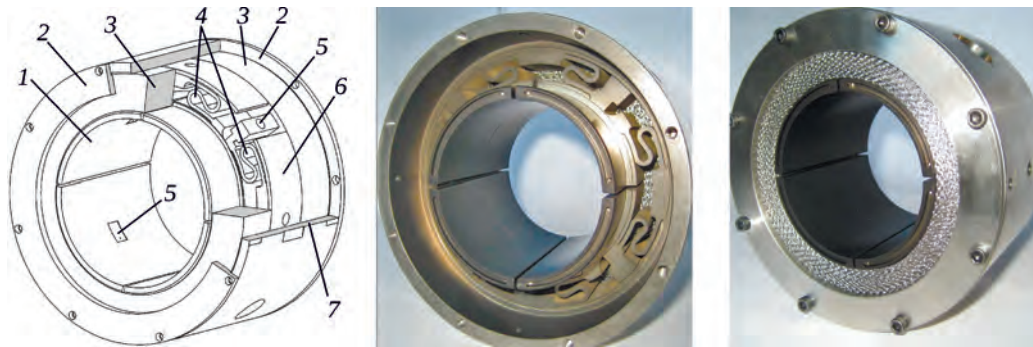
Принципиальная схема подшипника с колодками и демпферами из металлической сетки: 1 – колодка; 2 – фланец; 3 – сетка; 4 – пружины; 5 – канавка подачи смазки; 6 – кольцо; 7 – обойма
